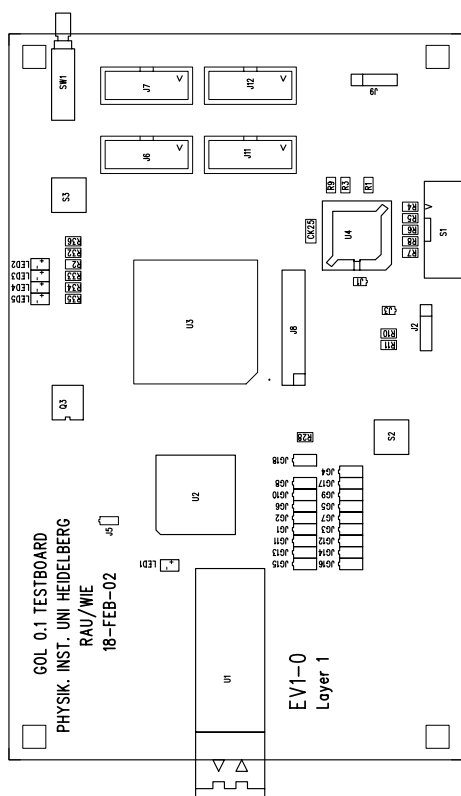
GOL 0.1 PCB EV1 Bestückungsplan oben.
